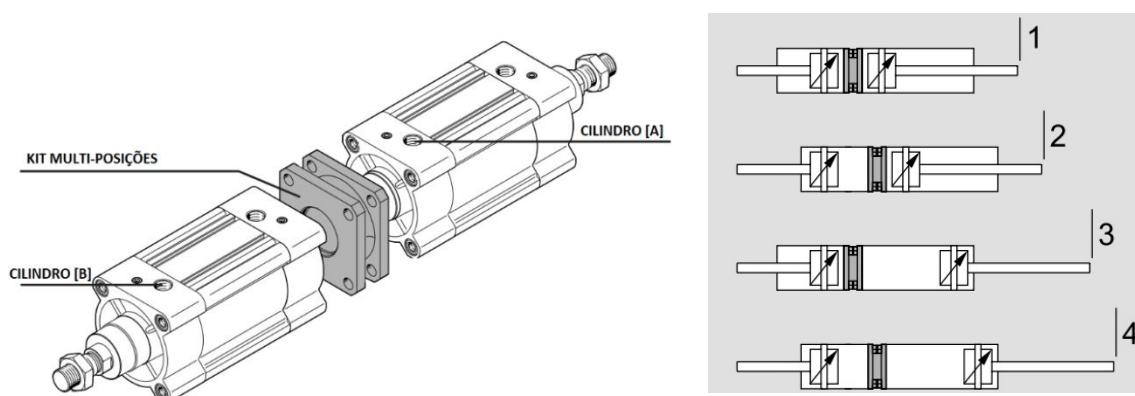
Montagem de dois cilindros com o *Kit* multi-posições e posições do conjunto (Festo, 2013)
